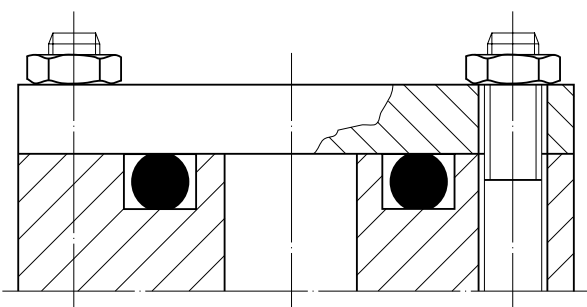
Flanschdichtung: O-Ring axial verpresst
